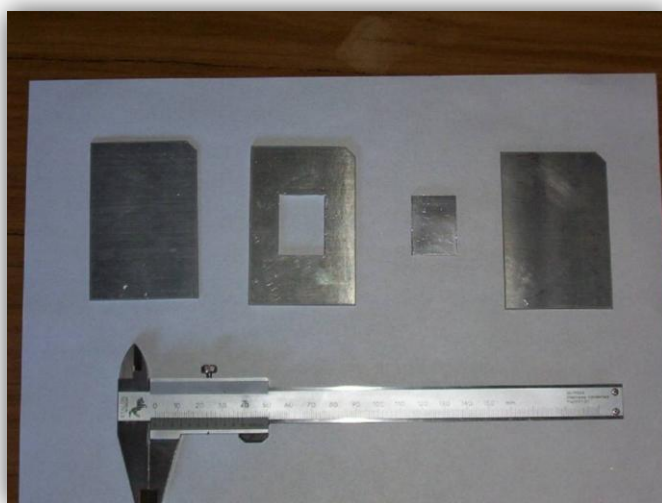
Tapas, marco y núcleo que conforman el conjunto a ser soldado lateralmente.
